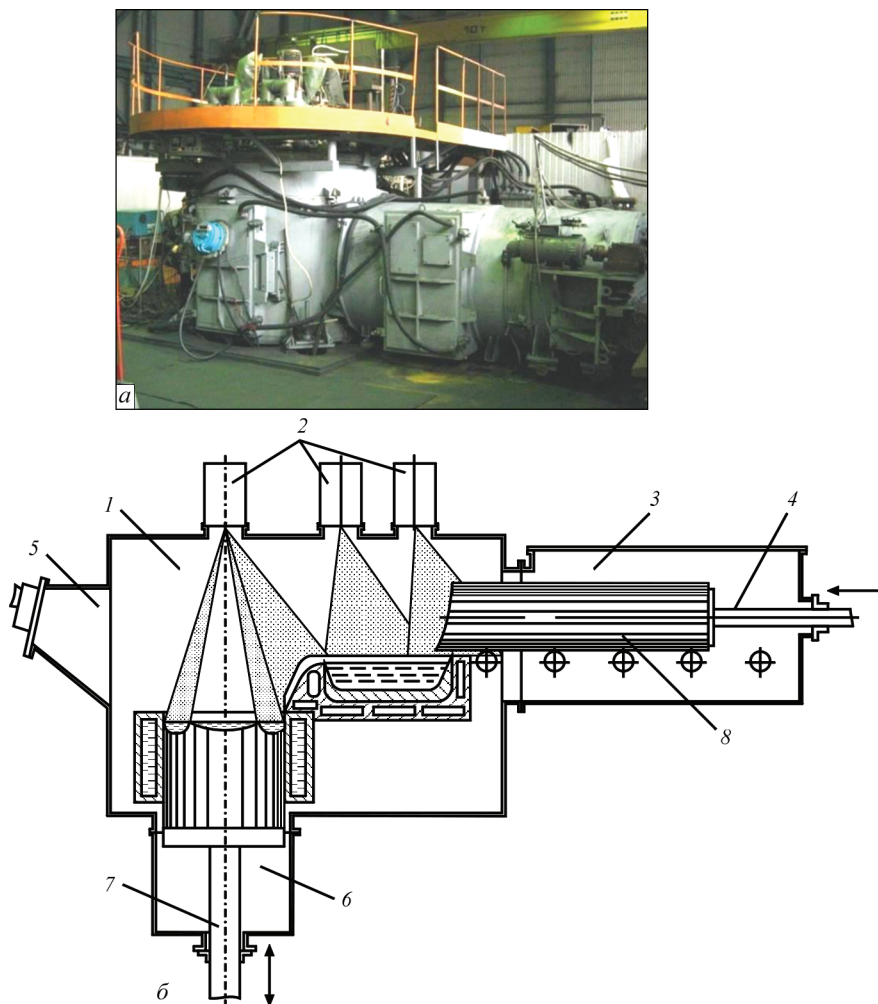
Зовнішній вигляд (а) і схема установки (б) УЕ-121: 1 — камера плавки; 2 — електронні гармати; 3 — камера заготовки; 4 — механізм подачі заготовки; 5 — оглядова система; 6 — камера зливка; 7 — механізм витягування зливка; 8 — рольганг
